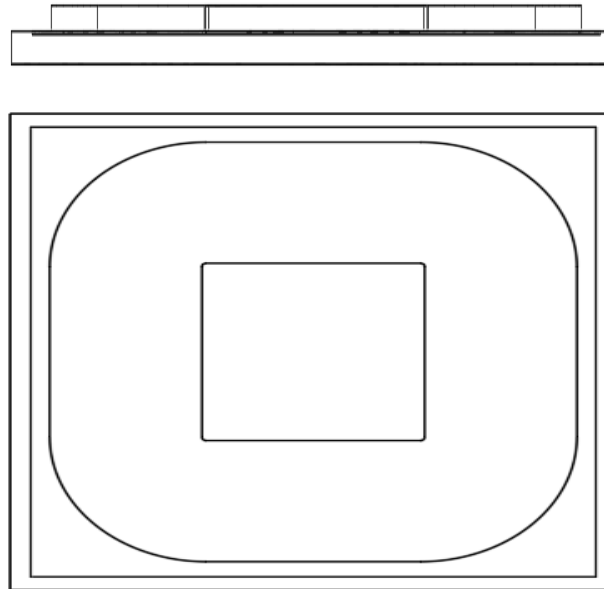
Alzado y planta del secundario del sistema de 50 KW
